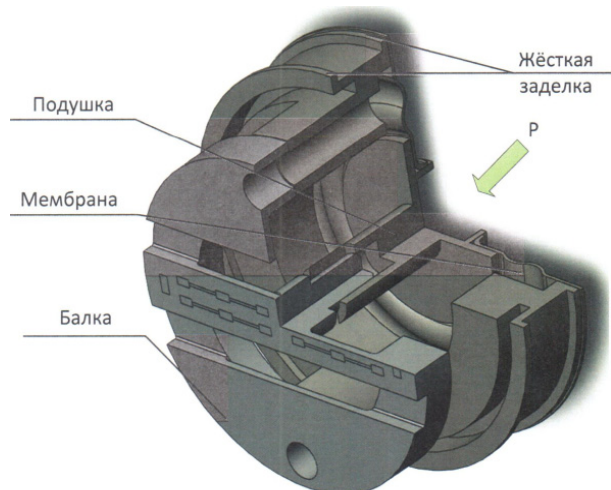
Мембранный блок, представляющий собой сварную конструкцию мембраны, подушки и балки
